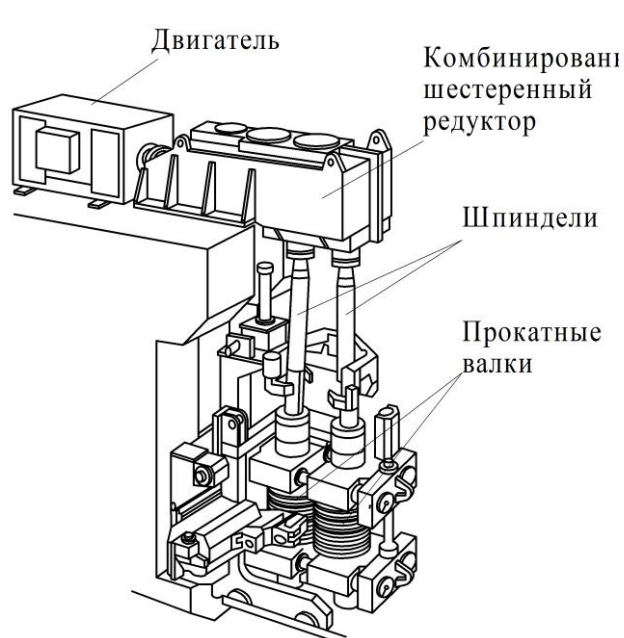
Общий вид привода прокатной клетки с комбинированным редуктором
